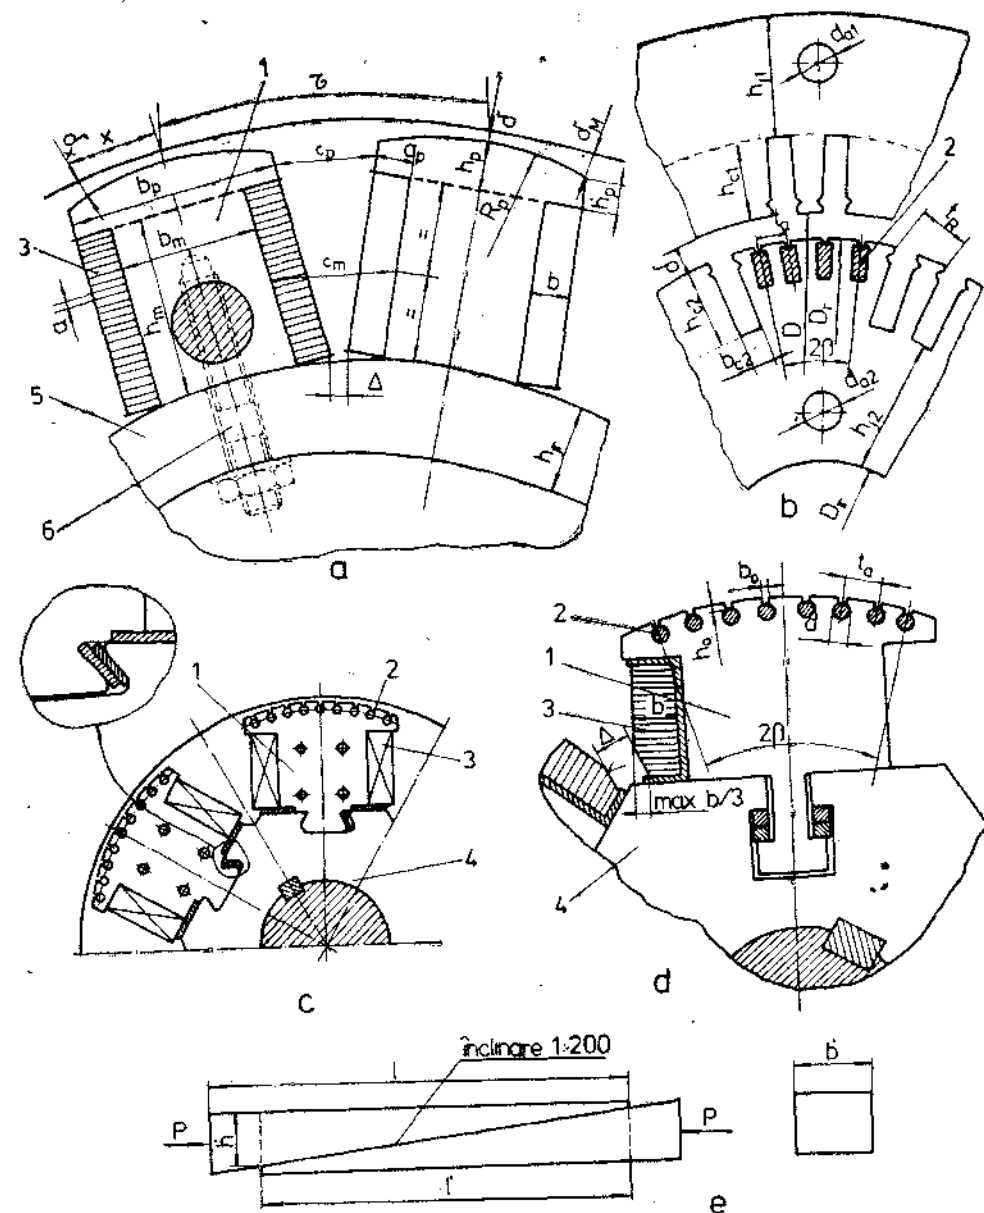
Construcția rotorului mașinilor sincrone cu poli aparenti fixați cu prezoane (a), fixați cu coadă de rîndunică (c) sau fixați cu coadă în T (d), prin intermediul penelurilor înclinate (e) și construcția mașinilor sincrone cu poli înecați (b):
